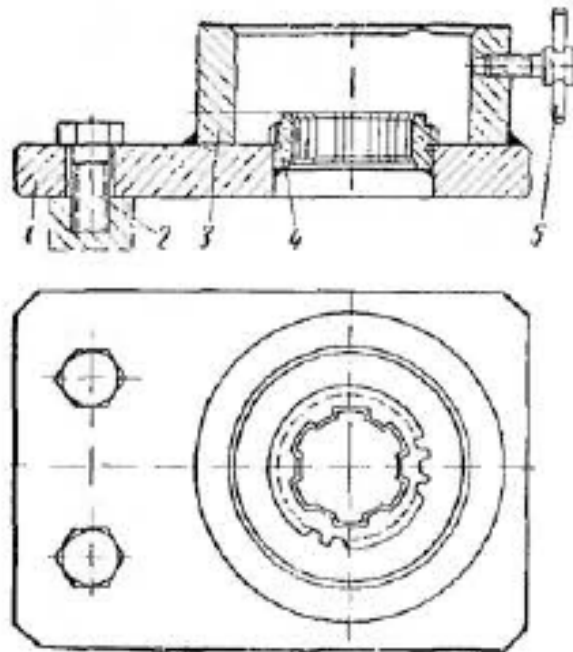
Підставка для розбирання ведучого вала коробки передач:
